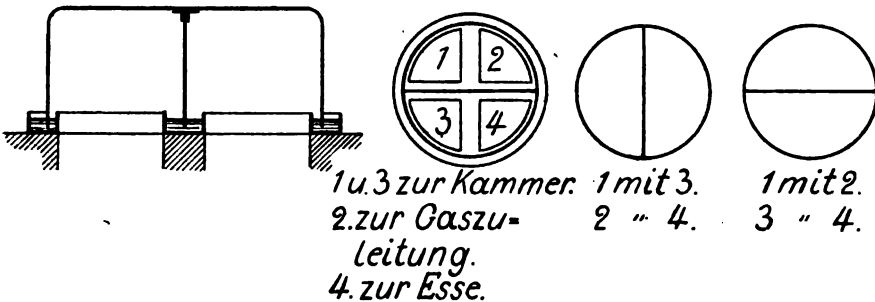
Glockenventil älterer Ausführung (schematisch gezeichnet).
